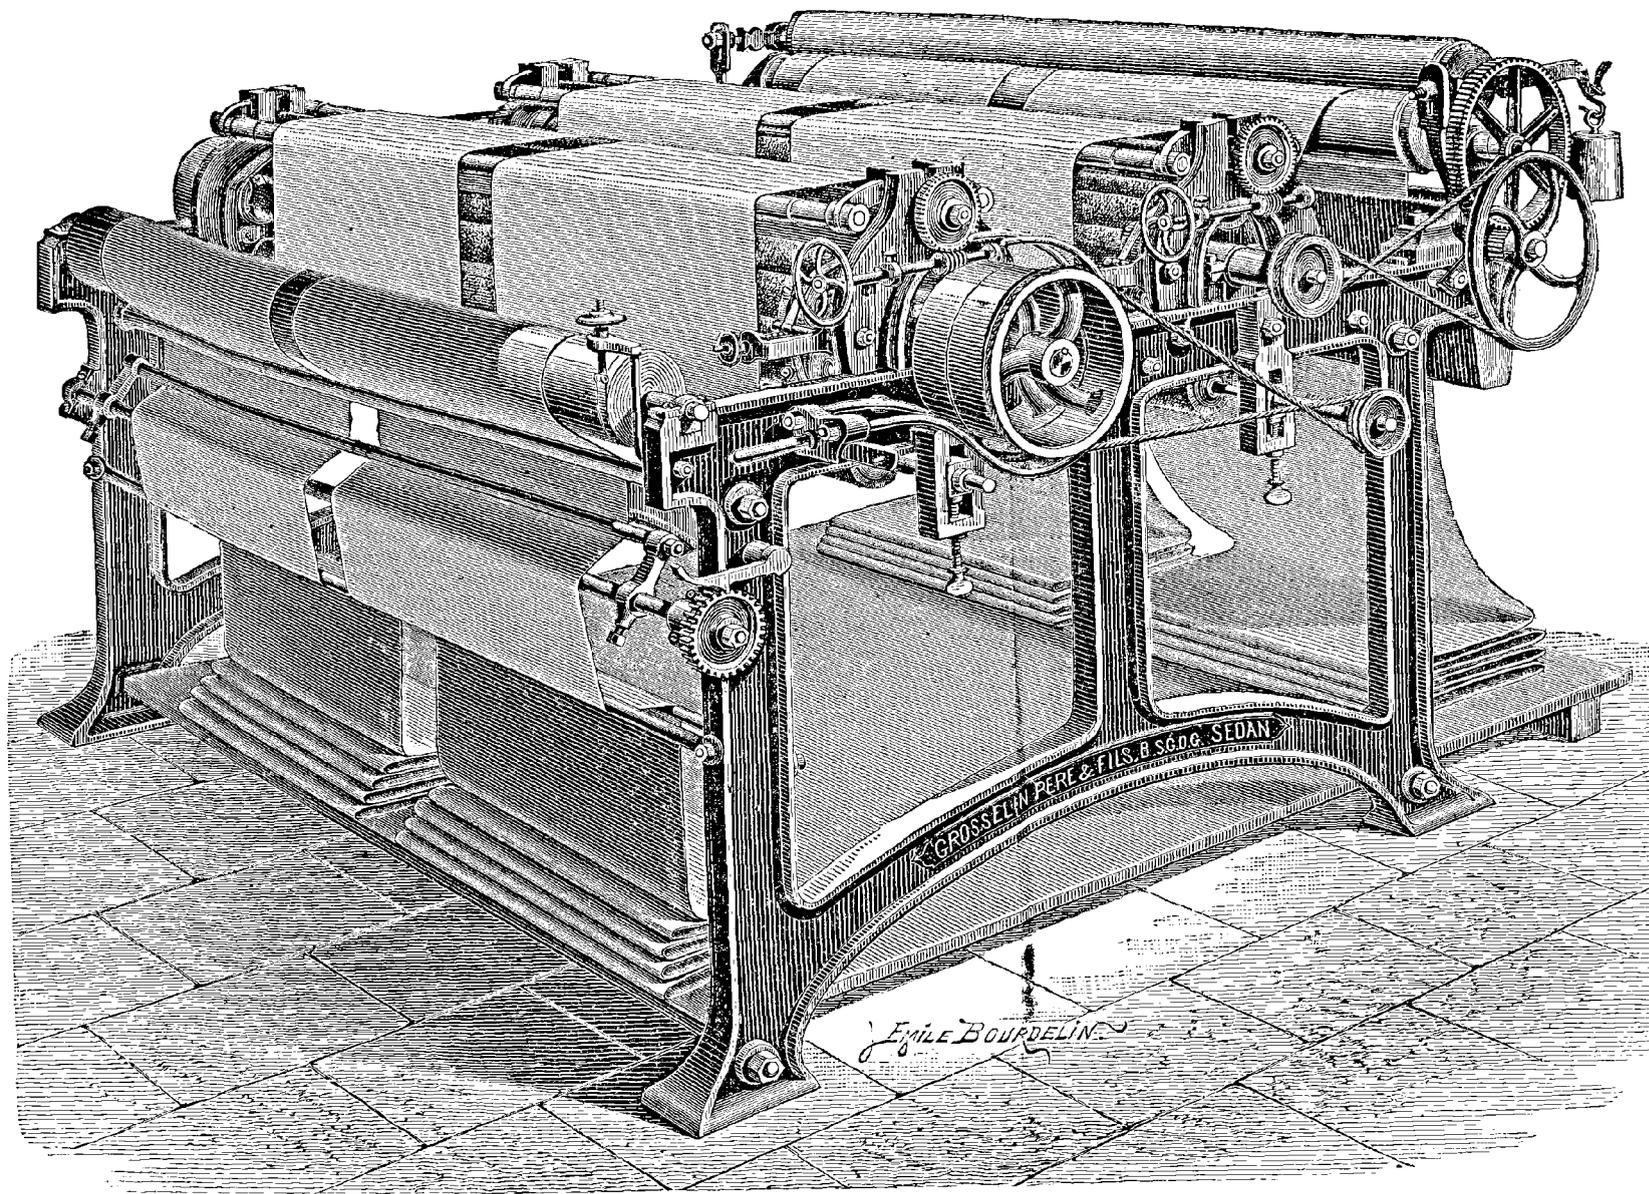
Machine à lainer à deux tambours, de MM. Grosselin père et fils
